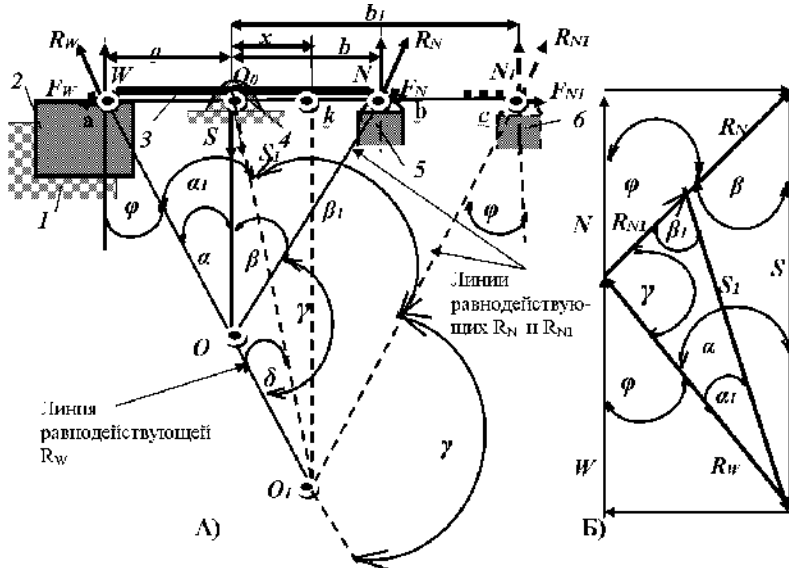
Схема сил и многоугольник сил, действующих на «прямой» рычаг: 1-опора заготовки; 2- заготовка; 3- рычаг, 4- опора рычага, 5- плунжер, 6- положение удлиненного левого плеча рычага
